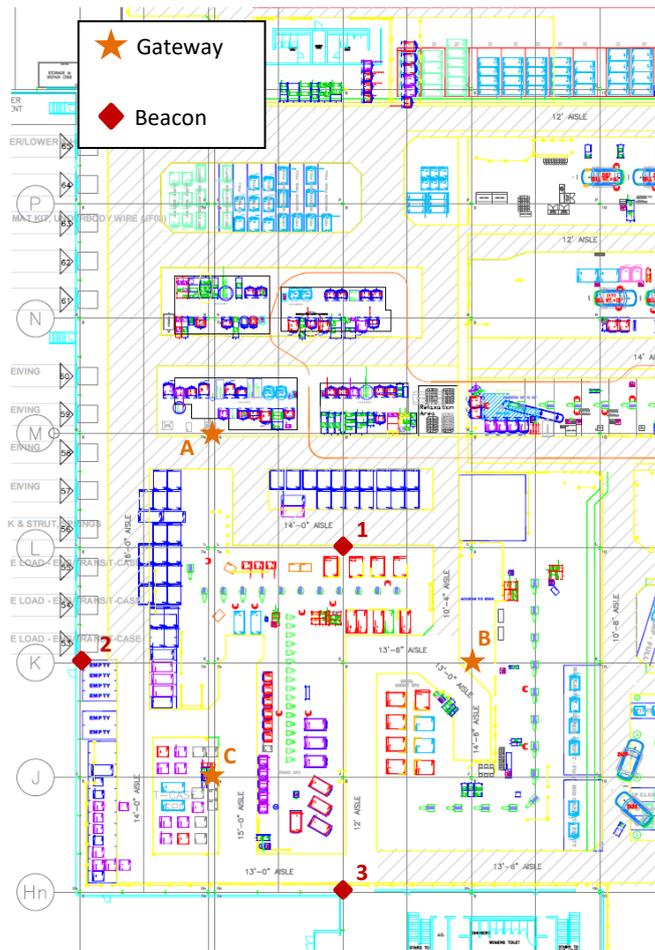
Posizione Gateways e Beacons nella Model Area
